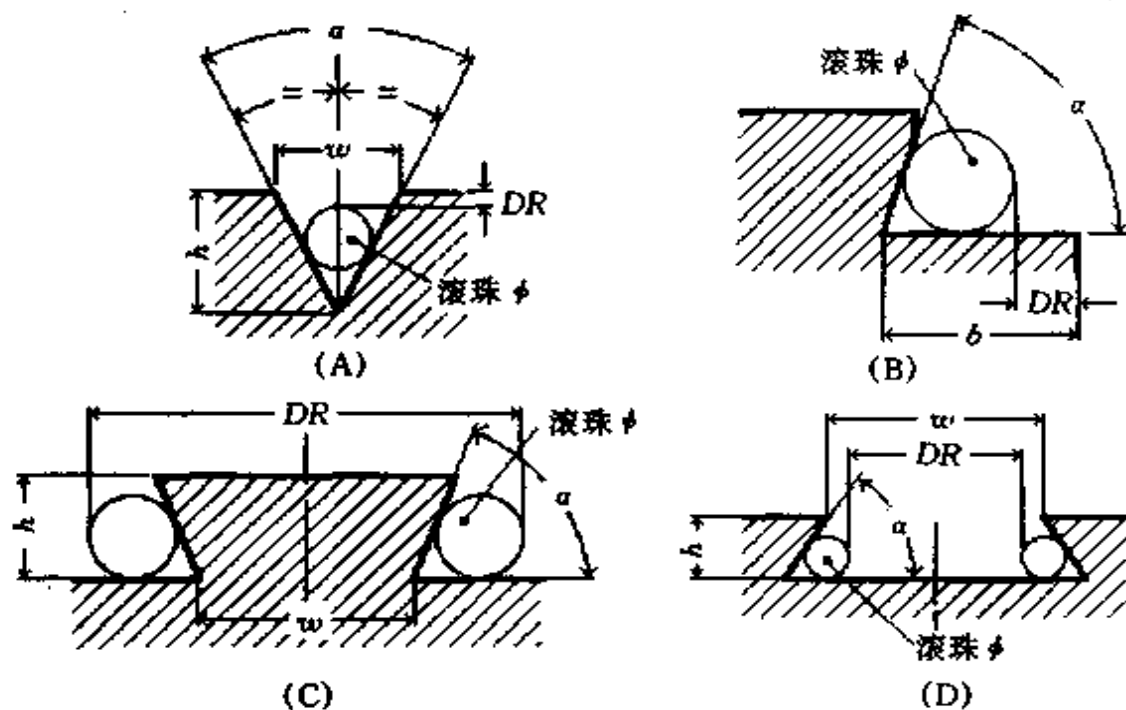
用滚珠决定的 DR 尺寸标注带角度的表面尺寸
